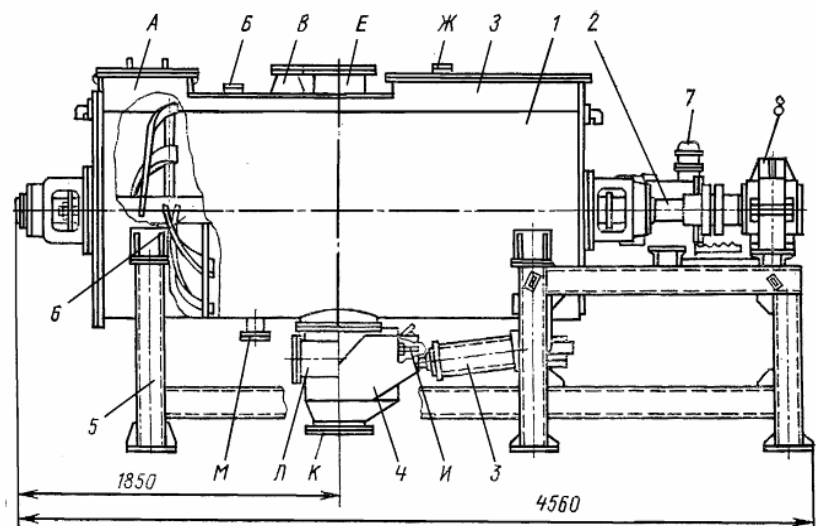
Схема ленточного смесителя типа Лн-2,0
